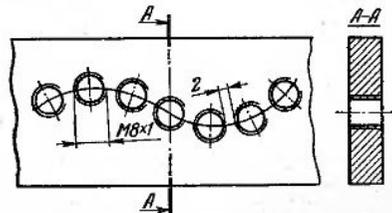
Трещина с резьбовыми отверстиями под свертыши.
